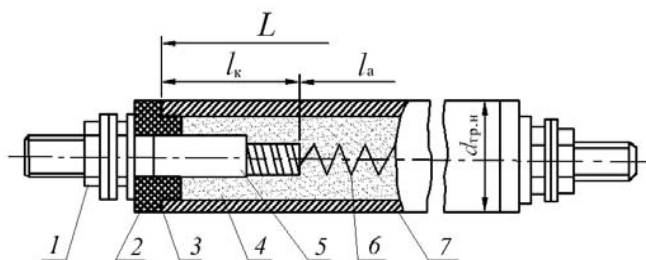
Типовая конструкция трубчатого нагревателя:
